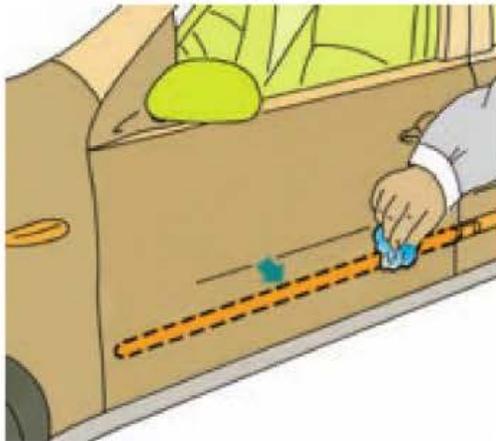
Desengrasado de la zona de contacto de la moldura.
